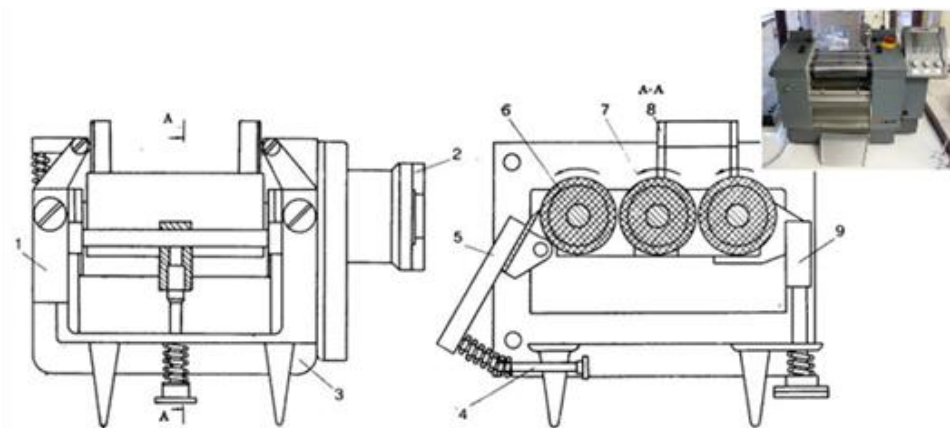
Схема трехвалковой машины ЕХАКТ [8]. 1 – корпус подшипников; 2 – полумуфта; 3 – станина; 4 – поджим; 5 – скребок; 6, 7 – валок; 8 – бункер; 9 – регулятор зазора.
